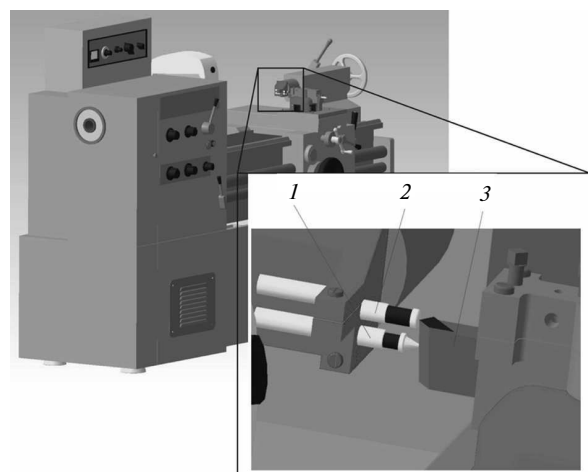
Устройство для измерения размерного износа инструмента на токарном станке:
